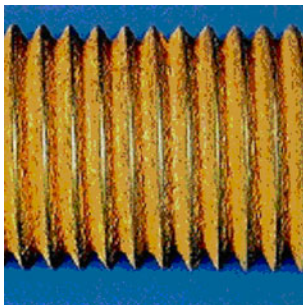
erZ) Beispiel einer Flächenkorrosion an einer Schraube (Bosshard)
